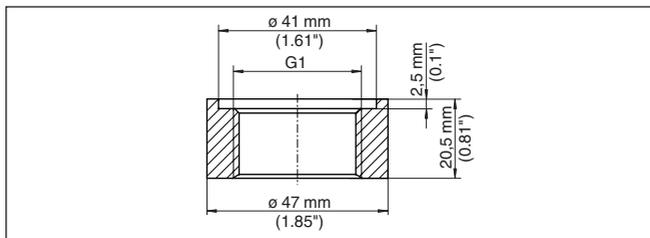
Dimensions raccord à souder filetage G1 (DIN 3852-X)
